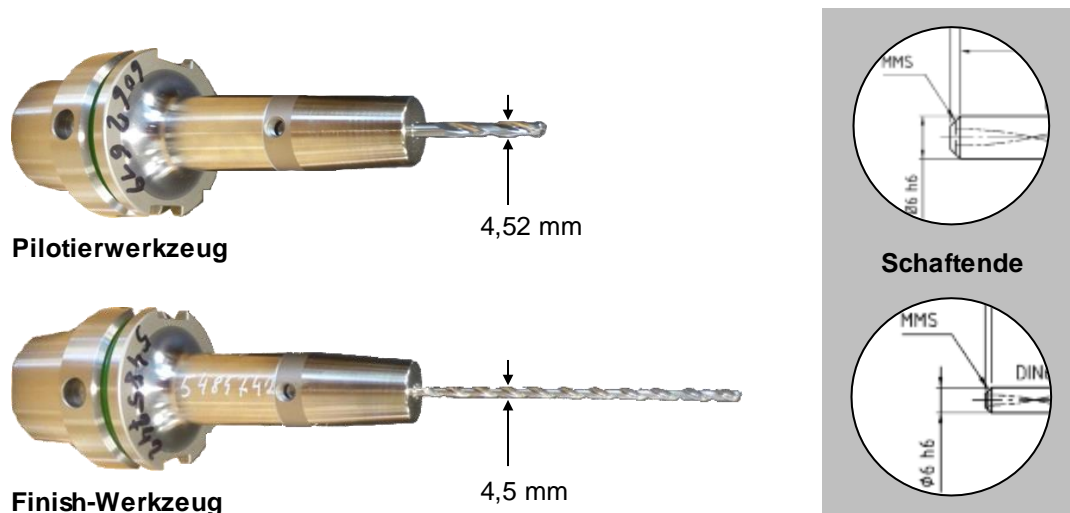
Finaler Stand der MMS-Werkzeuge für die Bearbeitung der Ölbohrung mit $D = 4,5$ mm im KG B48
